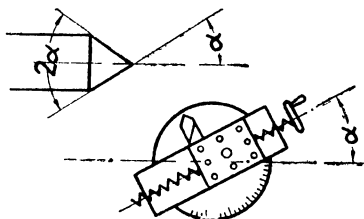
Схема установки детали для обтачивания конической поверхности способом поворота верхней части суппорта.
